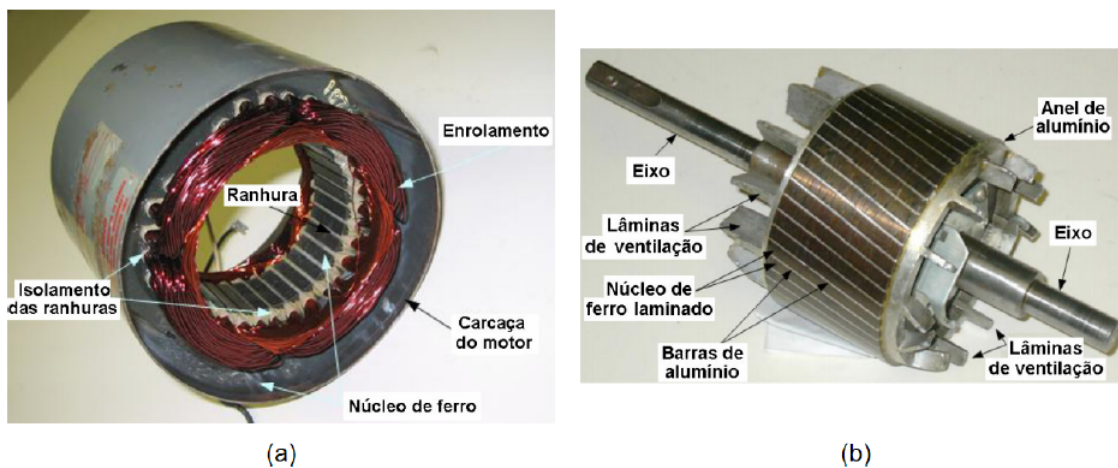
Componentes elétricos básicos de um motor de indução: (a) estator e (b) rotor. Adaptada de [5]
